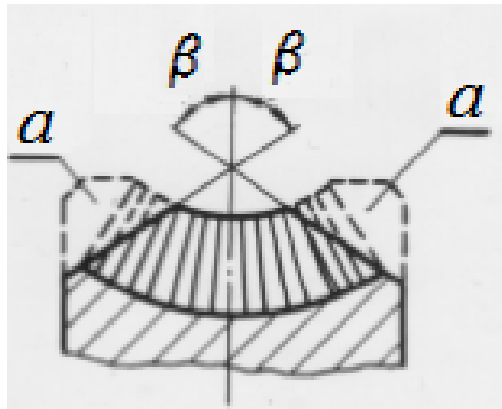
Обкатна зона робочої поверхні зуба колеса.
